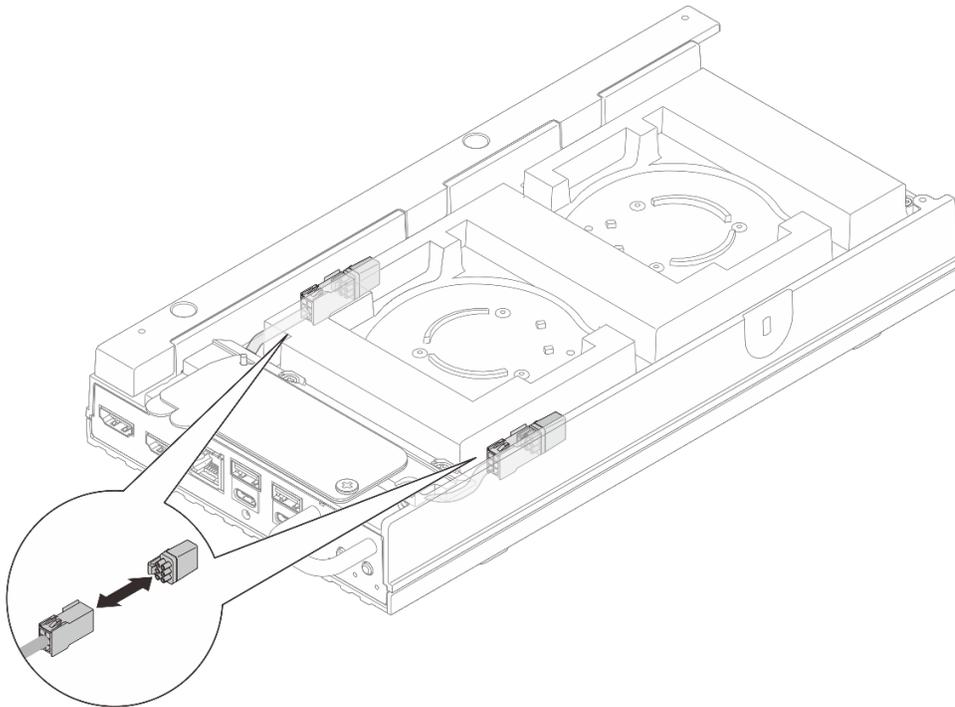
Installation d'un obturateur antipoussière pour câble de passerelle de ventilateur
